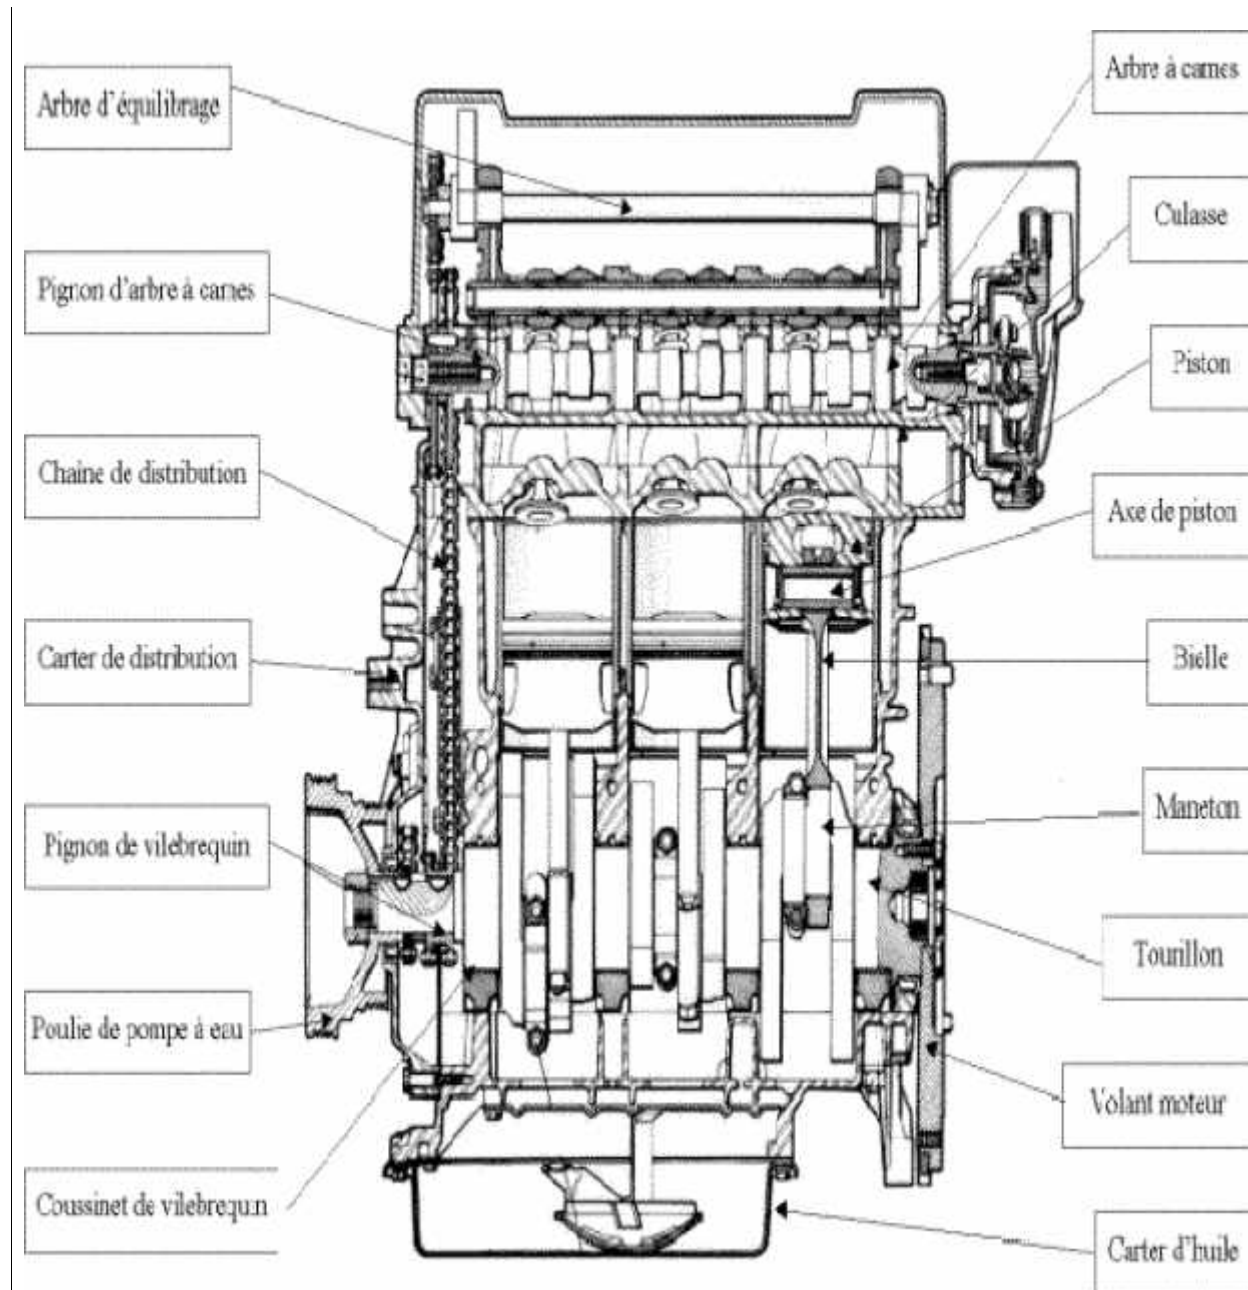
Schéma d'ensemble d'un moteur thermique [3].
